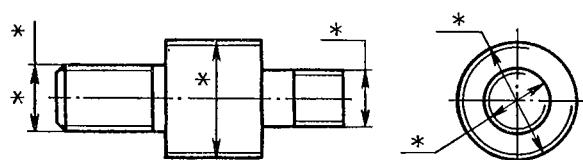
Места нанесения обозначения резьбы на стержне
